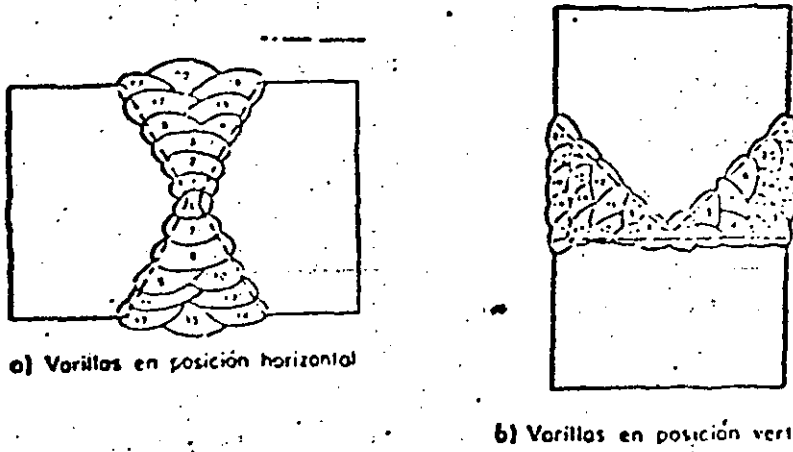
SECUENCIA PARA LA COLOCACION DE LOS CORDONES DE SOLDADURA
